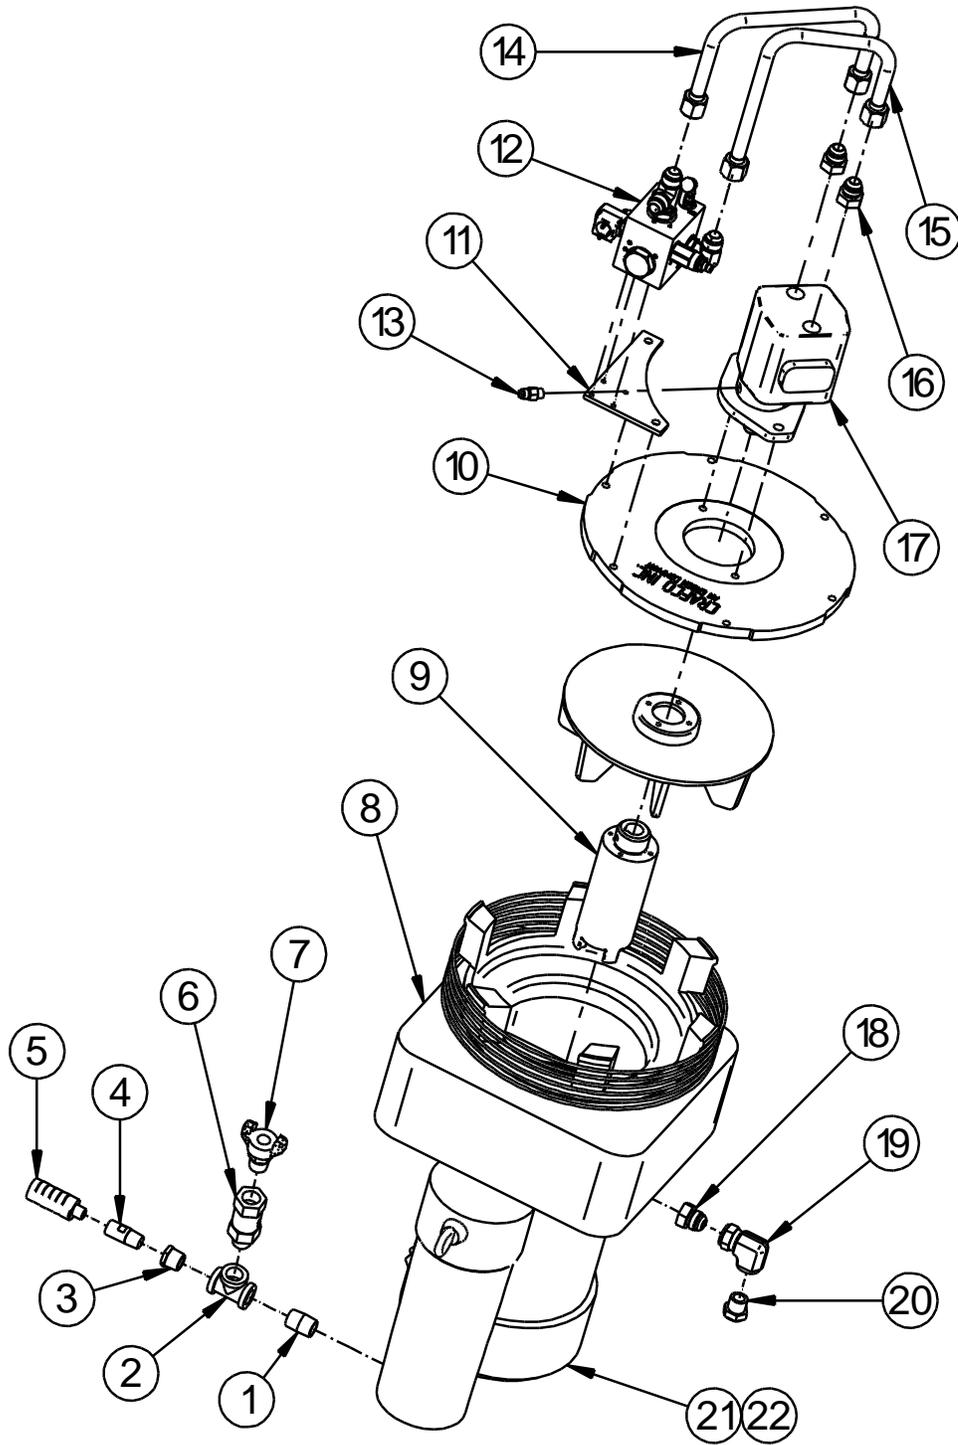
Conjunto del Compresor de Aire: PN 47480N (47400)
